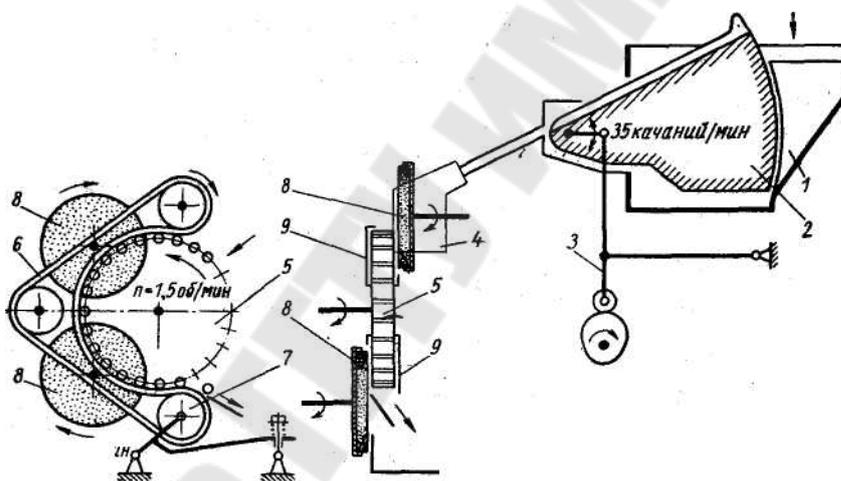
Принципиальная схема полуавтомата для зачистки втулок клапана с двух торцов: 1- загрузочный бункер; 2 - качающийся нож; 3- привод ножа; 4- приспособление для кантовки и укладки отливок на питающий диск; 5- питающий диск; 6- прижимная цепь; 7- натяжной ролик; 8- шлифовальные круги; 9- упорные планки.
